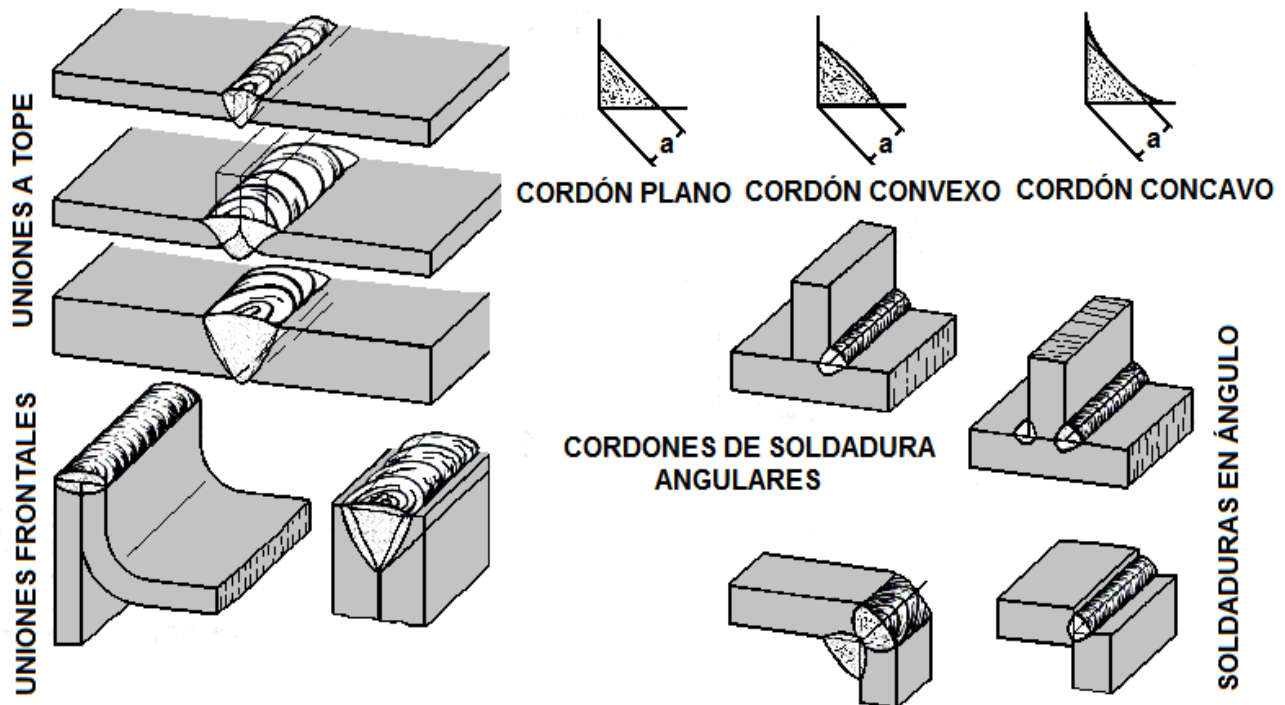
Diferentes tipos de uniones soldadas (7, 18, 28)
